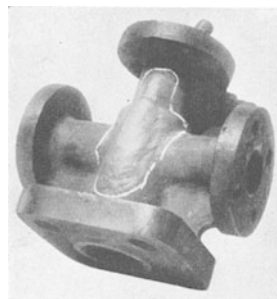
Geschweißtes Bronze-Ventilgehäuse.
